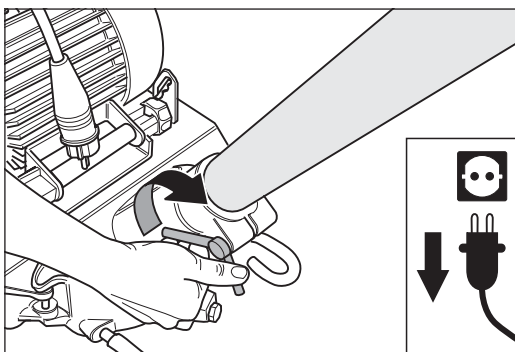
Nach dem Einbau des Führungsrohrs die Flügelmutter am Maschinengehäuse sorgfältig festziehen.
